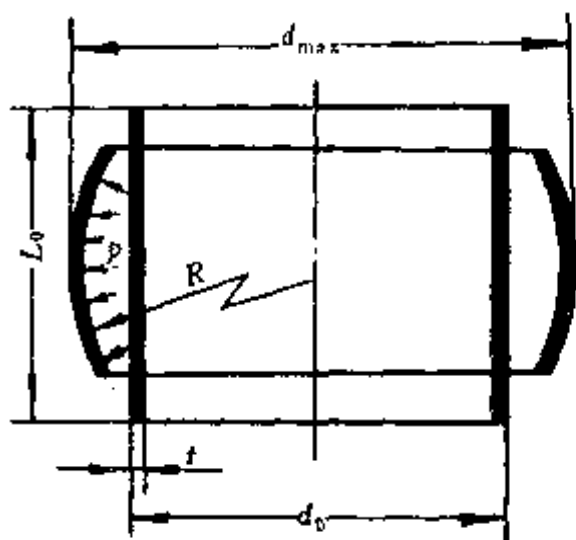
圆柱形空心毛坯胀形工件展开尺寸
